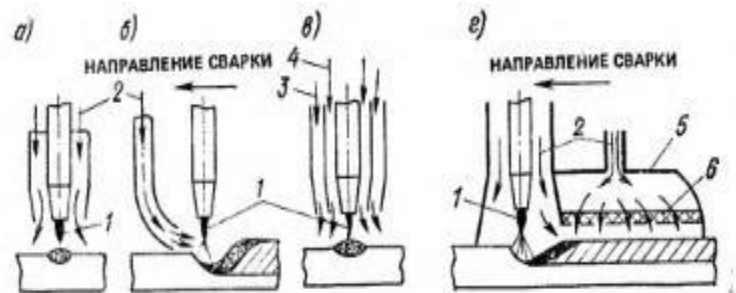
Схеми подачі захисного газу в зону зварювання а - центральна; б - бічна; у - двома концентричними потоками; г - в рухому камеру (насадку); 1 - електрод; 2 - захисний газ; 3, 4 - зовнішній і внутрішній потоки захисних газів; 5 - насадка; 6 - розподільна сітка.
